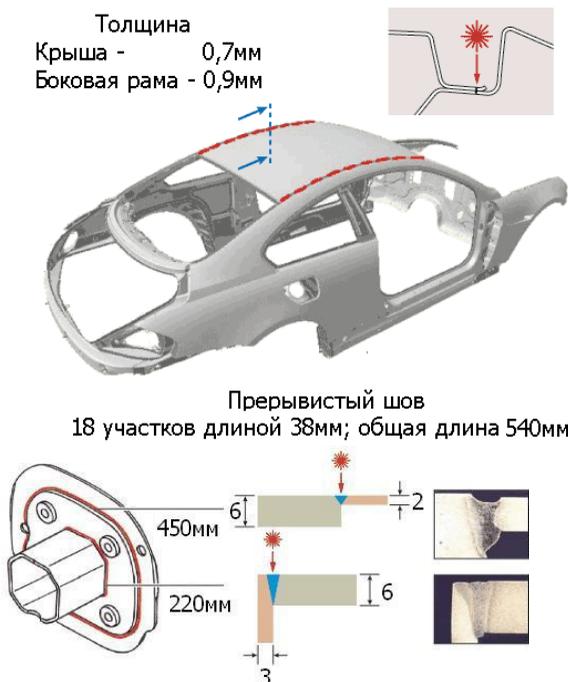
Сварной корпус автомобиля BMW 6 и детали кузова
